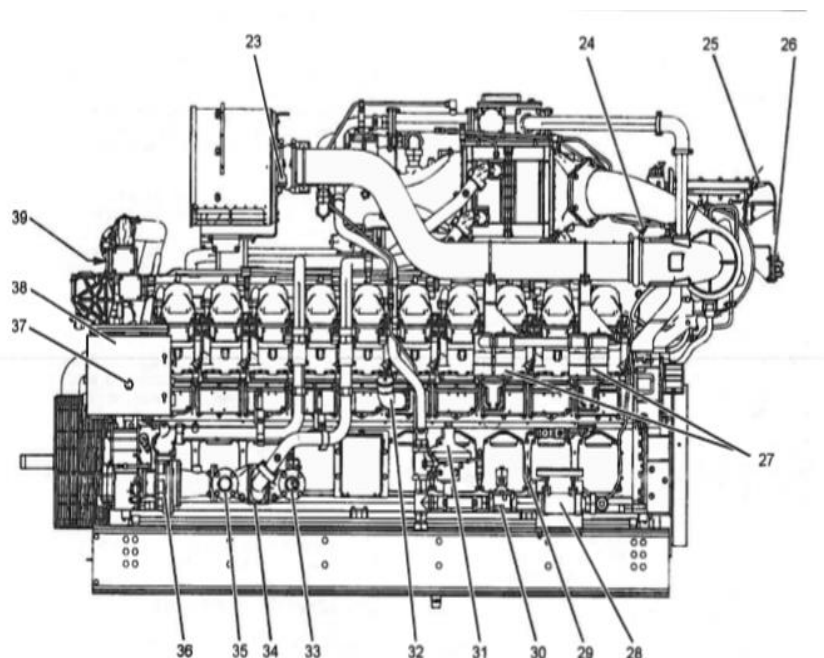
двигатель CAT G3520D вид двигателя слева
